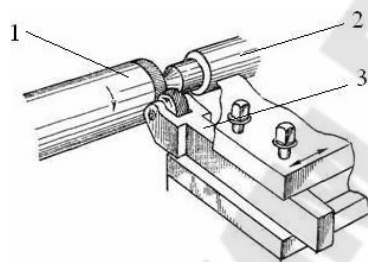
Схема процесса накатки: 1 – деталь; 2 – задняя бабка станка; 3 – державка с накатным роликом
